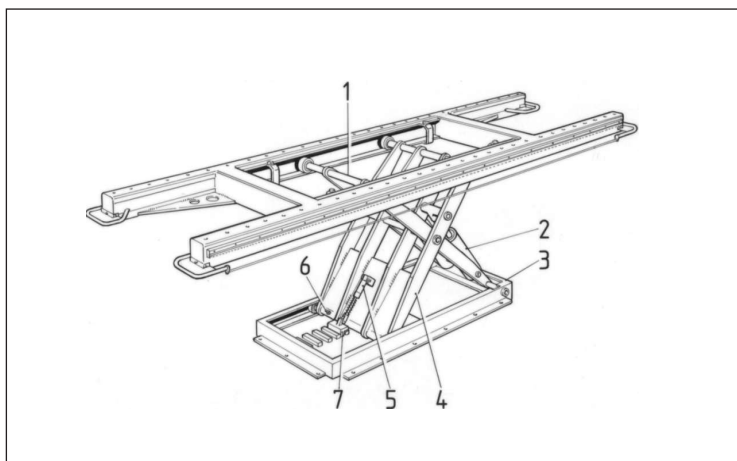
VISTA EN PERSPECTIVA DEL ELEVADOR
